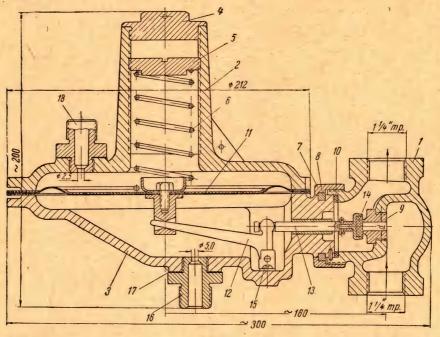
Регулятор давления типа РД-32 с наружным импульсным штуцером: I — тройник; 2 — верхняя часть корпуса; 3 — нижняя часть корпуса; 4 — крышка; 5 — нажимная гайка; 6 — пружина; 7 — нажимная гайка; 8 — полукольцо упорное; 9 — седло клапана; 10 — прокладка; 11 — мембрана; 12 — рычажный подаватель; 13 — шток; 14 — клапан, 15 — винт; 16 — импульсный штуцер $\varnothing^{1}/2$ "; 17 — прокладка; 18 — штуцер $\varnothing^{1}/2$ " β атмосферу.
